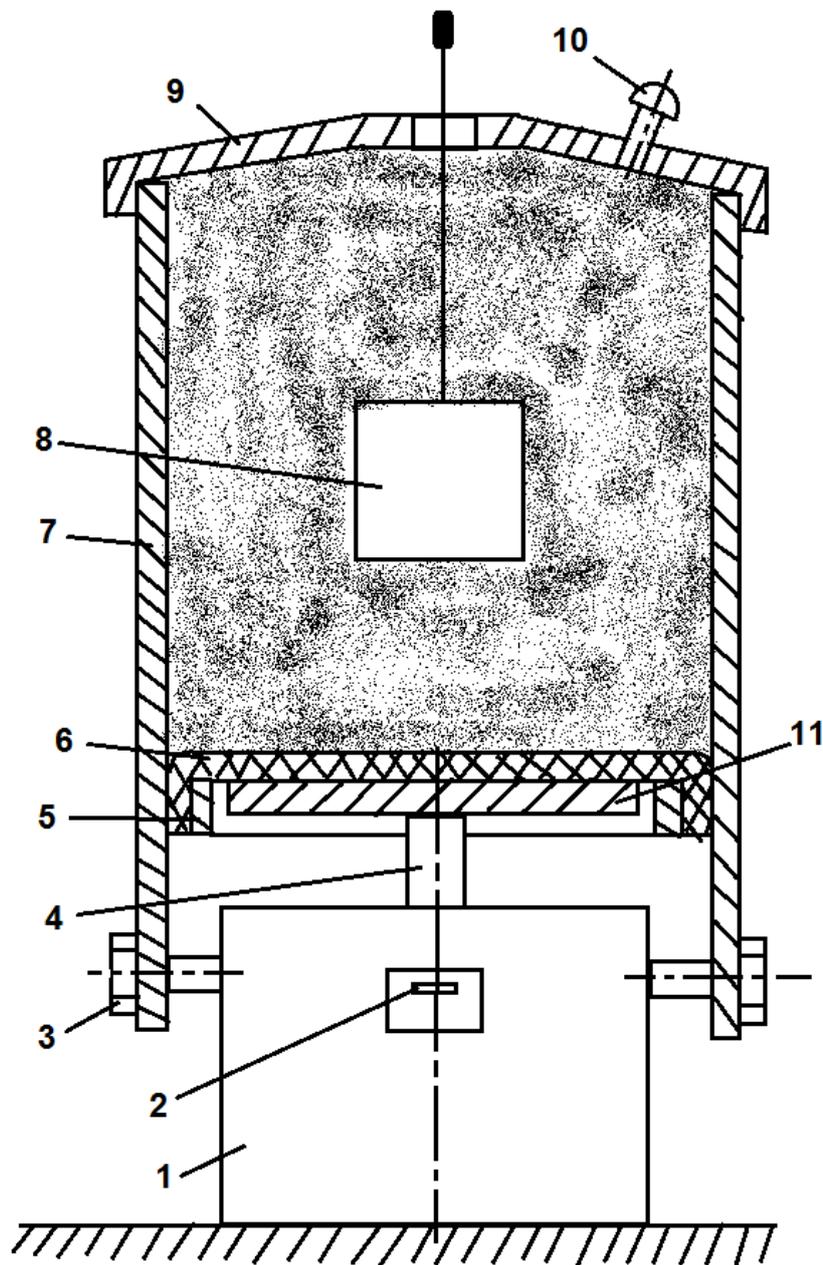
Схема установки для вибрационного напыления: 1 – корпус вибратора; 2 – выключатель; 3 – болт; 4 – вибратор; 5 – кольцо стальное; 6 – дно резиновое; 7 – цилиндр; 8 – обрабатываемая деталь; 9 – крышка; 10 – рукоятка; 11 – стальной диск
